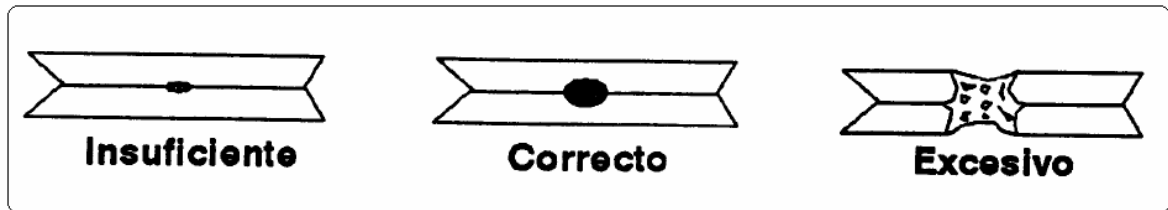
Relación entre la corriente de soldadura y el punto
